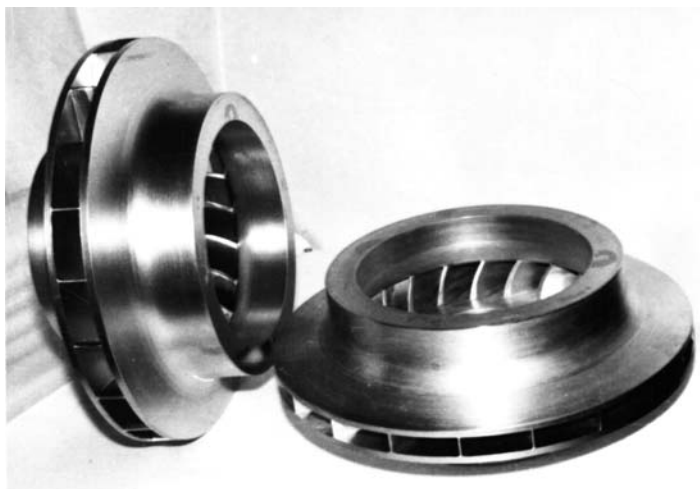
Паяні робочі колеса ЦКМ
